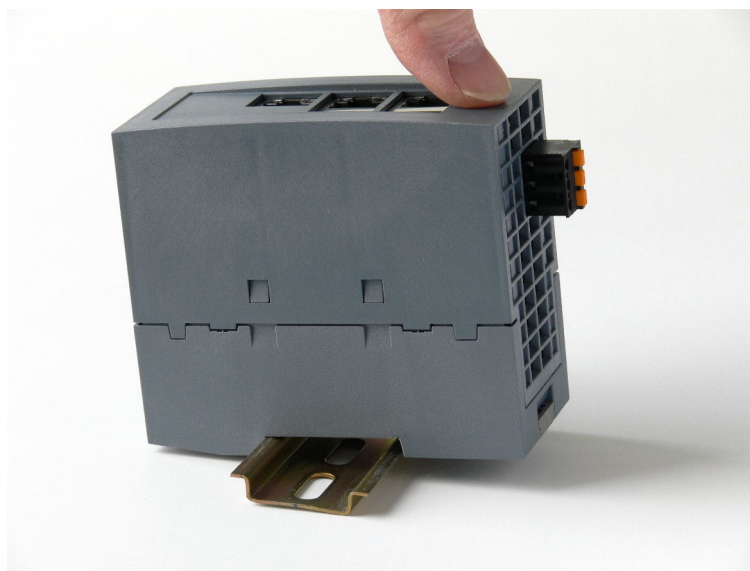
Montaje sobre un perfil DIN simétrico (35 mm)
